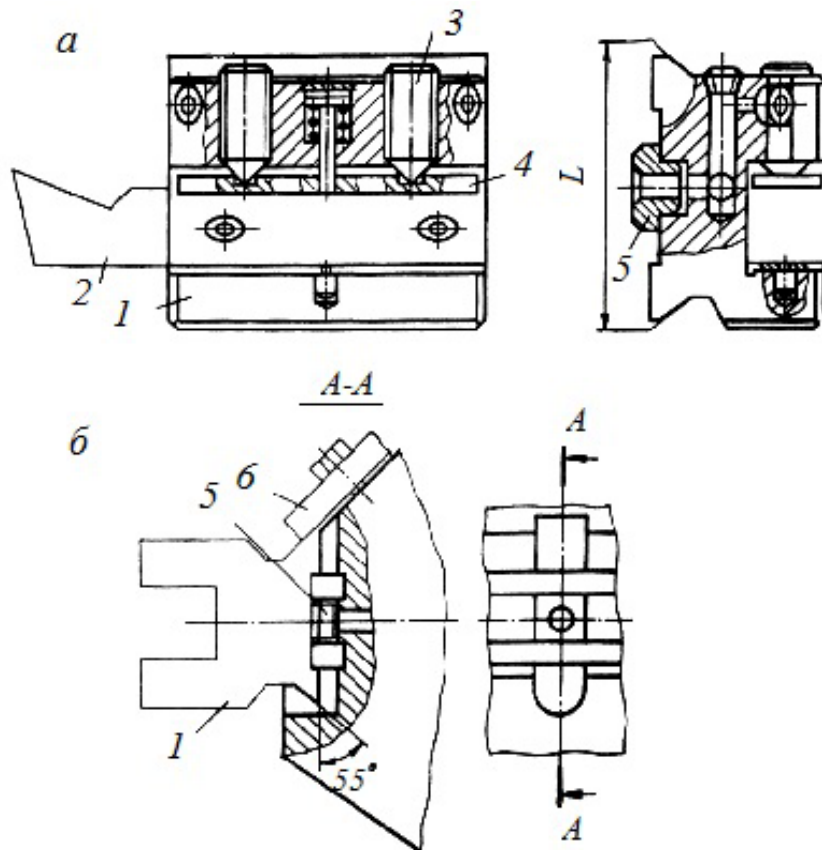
Схема соединения резцедержателя с базирующей призмой с револьверной головкой:
